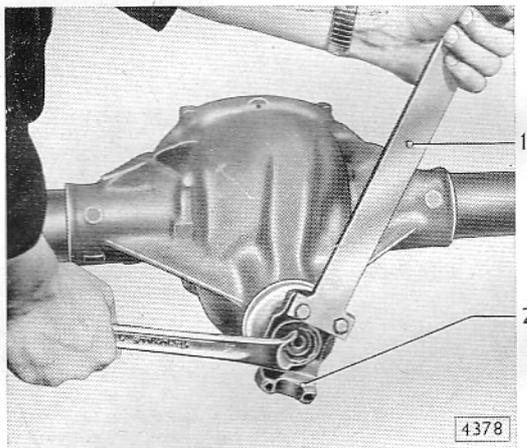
Flanschnutter des Antriebskegelrades abschrauben
